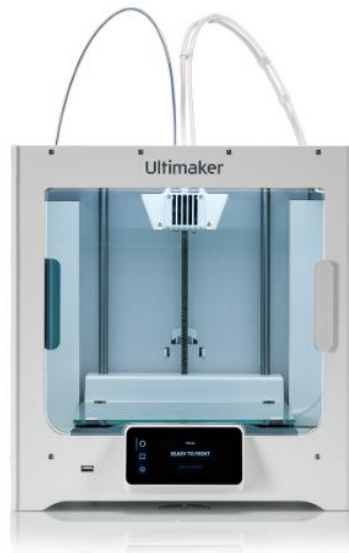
Màquina d'impressió Ultimaker S3. Font: Ultimaker
